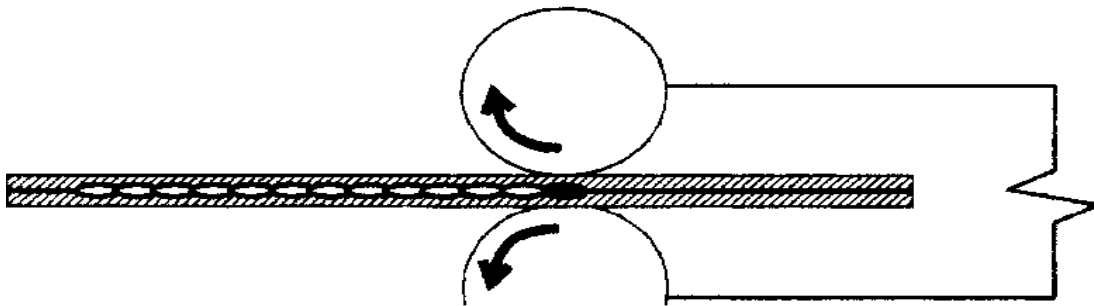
Esquemática gráfica da soldadura por roletes (RSEW) [20].
